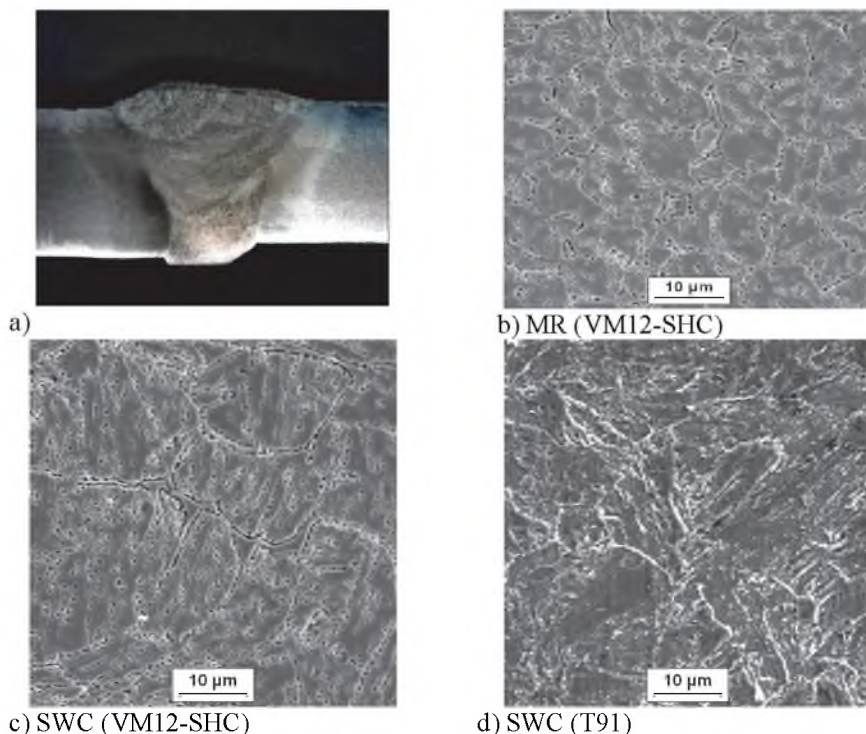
Wyniki prób pełzania materiału rodzimego i jednorodnego doczołowego złącza spawane-go ze stali VM12-SHC [11]
